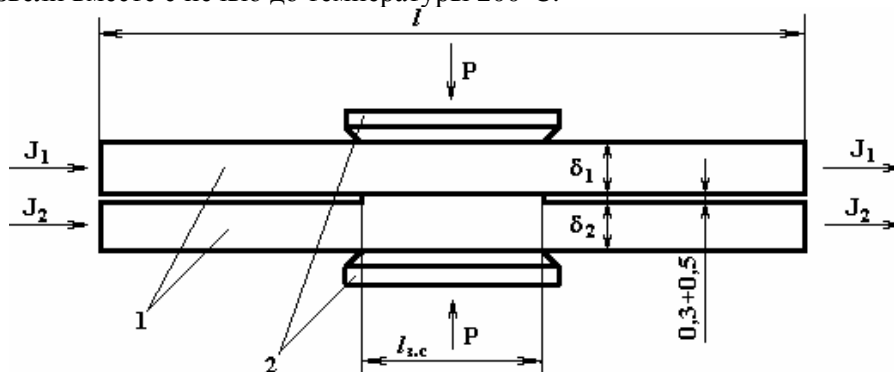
Схема обработки импульсным током свариваемых образцов. 1 – образцы; 2 – зажим приспособления;  $l_{з.с}$  – длина зоны сварки;  $l$  – длина образца;  $\delta_1, \delta_2$  – толщина образца
